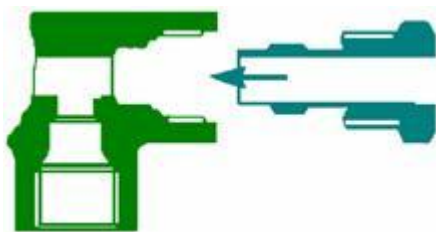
Sección transversal de racor de tipo bicono de compresión.
